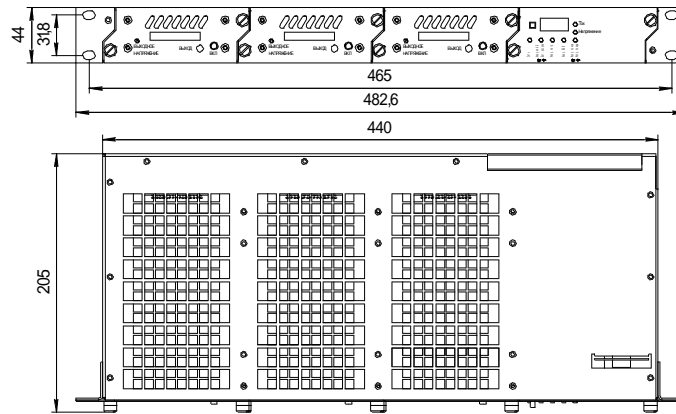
Габаритный чертеж УЭП-2К
